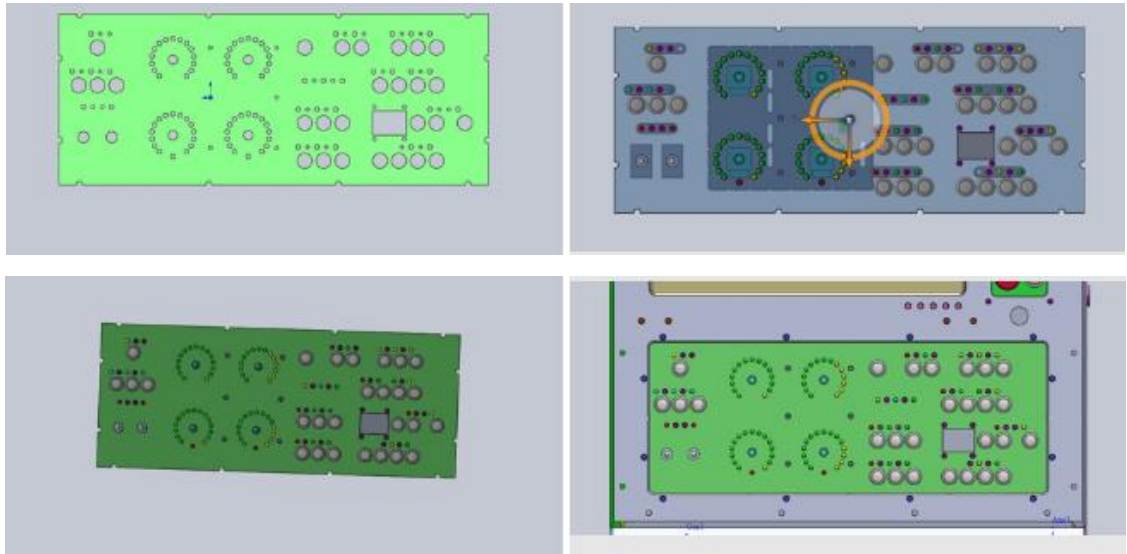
Бокова кришка корпусу пульта керування ЧПК
